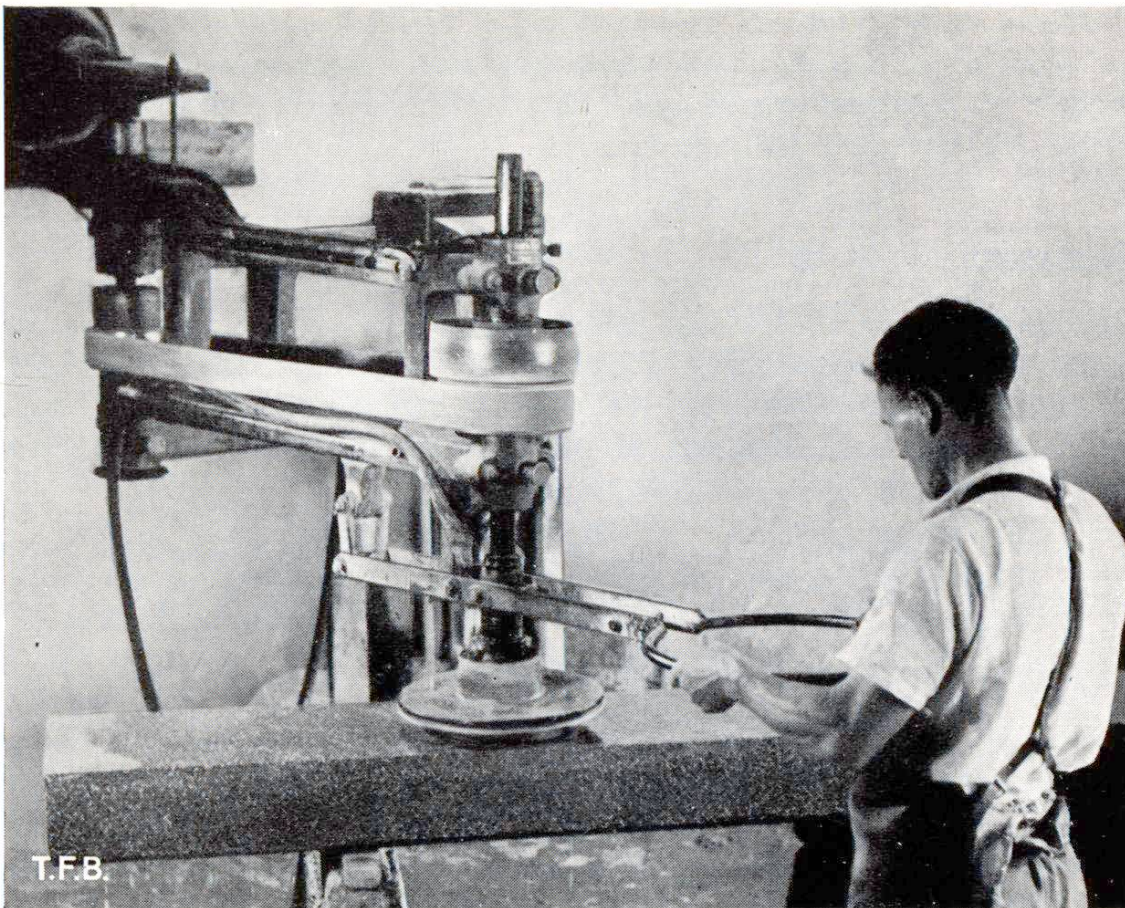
Polissage au moyen d'une machine à hauteur réglable fixée sur un bras mobile
